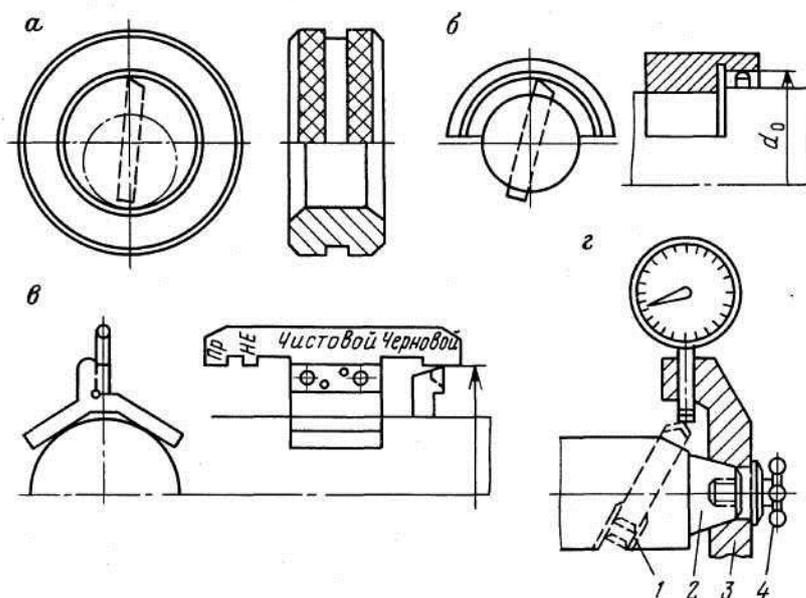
Способы установки резцов на оправках и борштангах: а - кольцевой шаблон; б - шаблон-полукольцо; в - предельный шаблон; г - индикаторный прибор (1 - регулировочный винт; 2 - корпус оправки; 3 - индикаторный прибор; 4 - винт)
